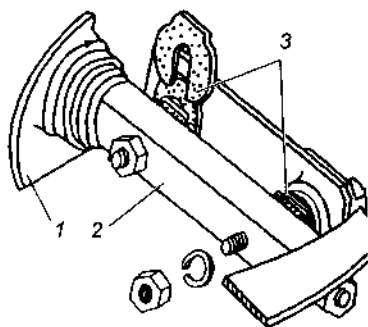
Регулировка колес автомобиля с рычажной подвеской: 1 — рычаг подвески; 2 — ось рычага; 3 — регулировочные скобы
